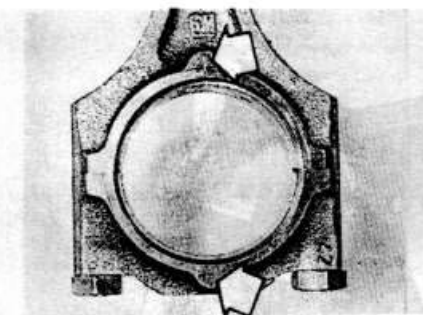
Бобышки (указаны стрелками) на шатуне и крышке большой головки должны быть направлены в сторону маховика — двигатель 1,6 л
